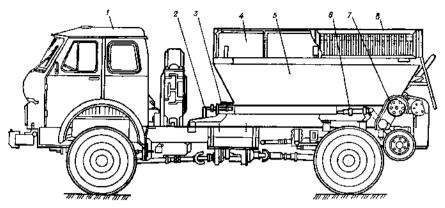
Пескосолеразбрасыватель ДМ-12: 1 — автомобиль МАЗ-509А; 2 — газоподводящий металлорукав; 3 — транспортер; 4 — съемный борт; 5 — кузов; 6 — пневмосистема; 7 — привод транспортера; 8 — предохранительная решетка
